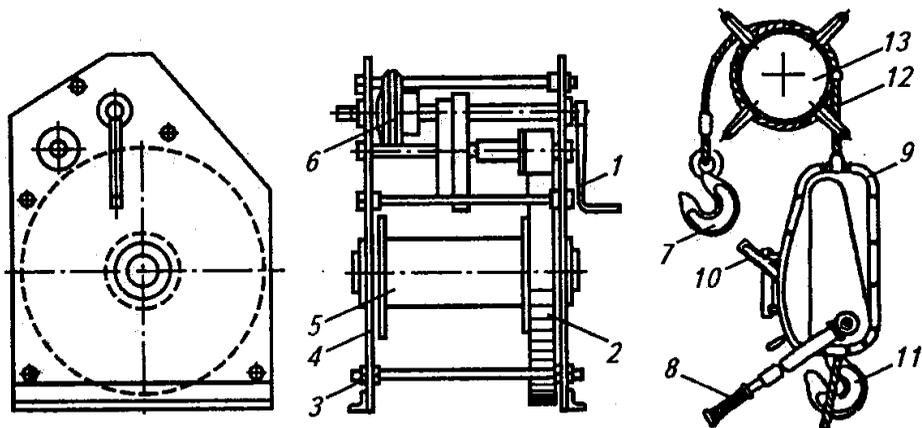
Лебедки ручные: а – с барабаном; б – рычажная; 1 – рукоятка; 2 – большое зубчатое колесо; 3 – стяжной болт; 4 – щека; 5 – барабан; 6 – храповое колесо с собачкой; 7 – катушка; 8, 11 – крюки; 9 – рукоятка обратного хода; 10 – рукоятка прямого хода; 12 – канат; 13– корпус лебедки
